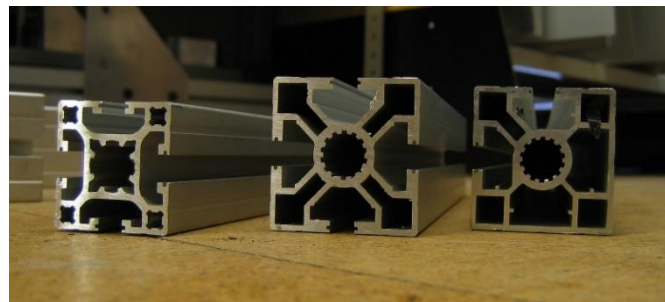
Engranajes y elementos producidos a partir de aluminio.
